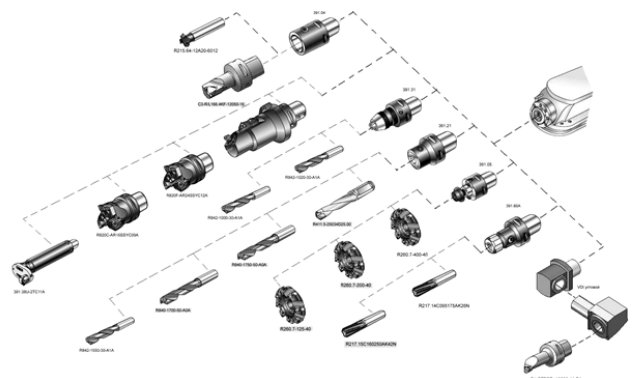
Виды инструментальной оснастки для обработки детали «Корпус редуктора»
